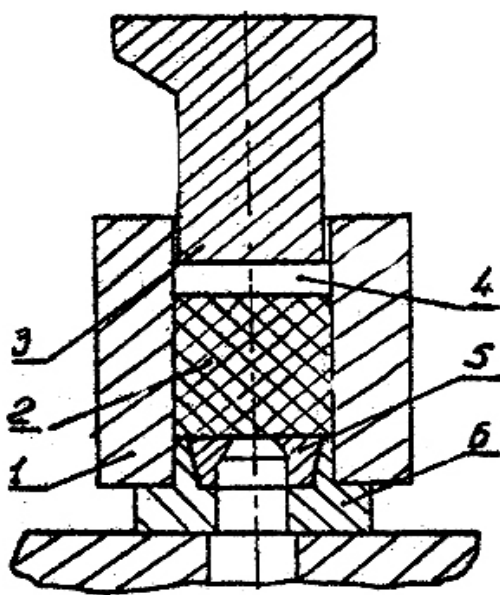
Схема установки для прессования прутков прямым и обратным способом.
